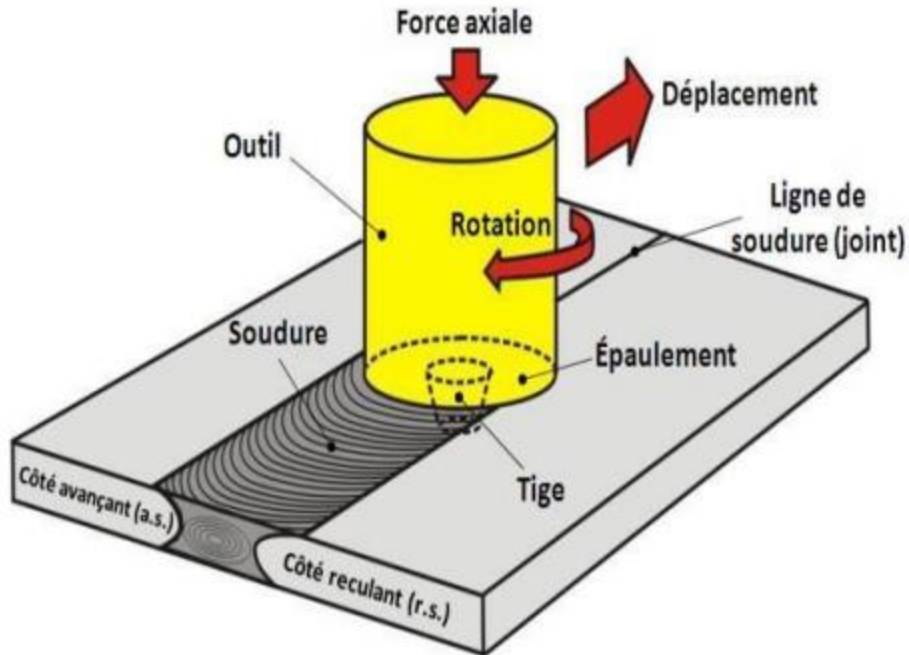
Illustration du procédé de soudage par friction et malaxage
